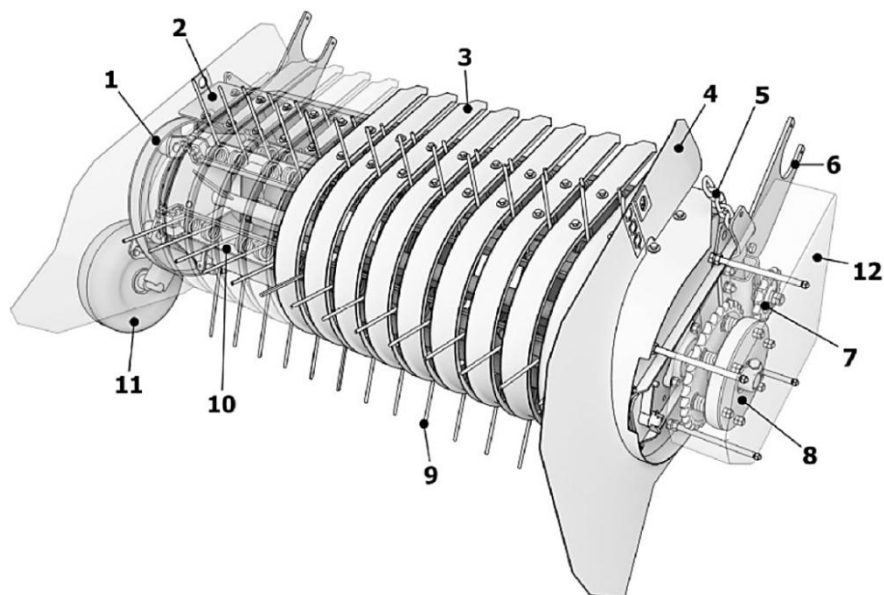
Подборщик: 1– беговая дорожка; 2 – рама; 3 – скат; 4 – боковой щит; 5 – транспортная цепь; 6 – установочный кронштейн; 7 – натяжная звездочка; 8 – муфта предохранительная; 9 – пружинный палец; 10 – граблина; 11 – копирующее колесо
